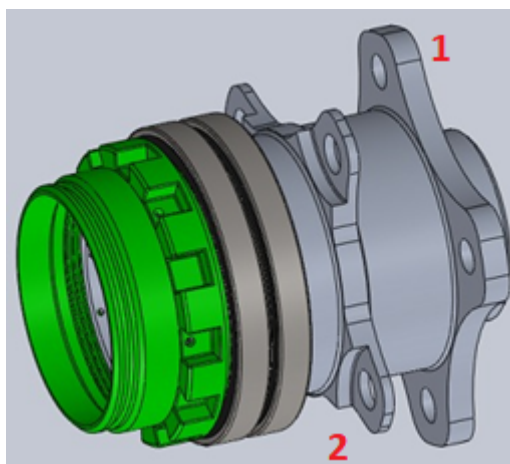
Imagem de modelo CAD do cubo de roda Apuama Racing 2017. (1) Flange de fixação para roda. (2) Flange de fixação para disco.
